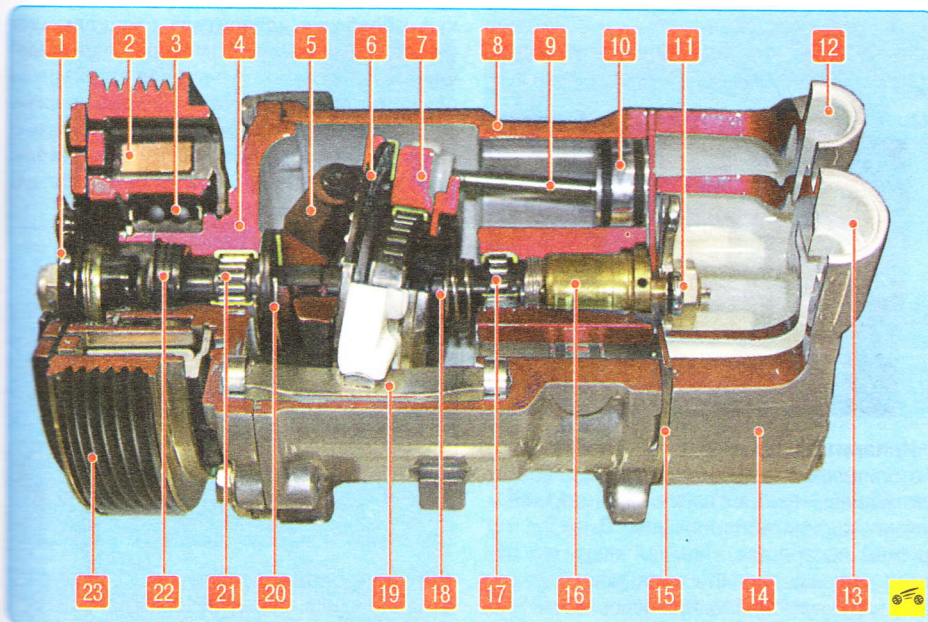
Компрессор кондиционера: 1 – прижимной диск; 2 – обмотка электромагнита; 3 – подшипник шкива; 4 – передняя крышка корпуса; 5 – рычаг обоймы наклонной шайбы; 6 – упорный роликовый подшипник наклонной шайбы; 7 – наклонная шайба; 8 – корпус компрессора; 9 – шатун; 10 – поршень; 11 – гайка крепления блока клапанов регулятора и упоров блока лепестковых клапанов; 12 – штуцер линии нагнетания; 13 – штуцер линии всасывания; 14 – крышка блока клапанов; 15 – блок лепестковых клапанов; 16 – блок клапанов регулятора подачи; 17, 21 – подшипники вала; 18 – вал наклонной шайбы; 19 – направляющий упор наклонной шайбы; 20 – упорный подшипник вала; 22 – сальник вала; 23 – шків привода
